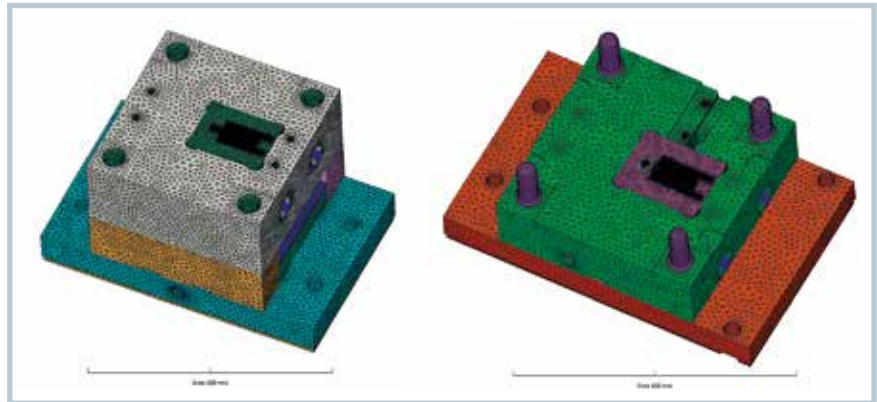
Das Probekörperwerkzeug wurde in Autodesk Simulation Moldflow Insight mit den maßgeblichen Werkzeugkomponenten tetraedervernetzt (links: Auswerferseite; rechts: Düsen- seite)
